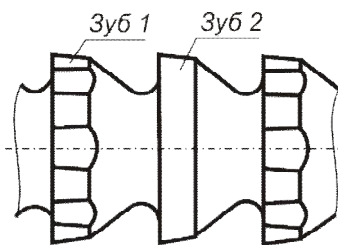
Режущие зубья круглой групповой протяжки
